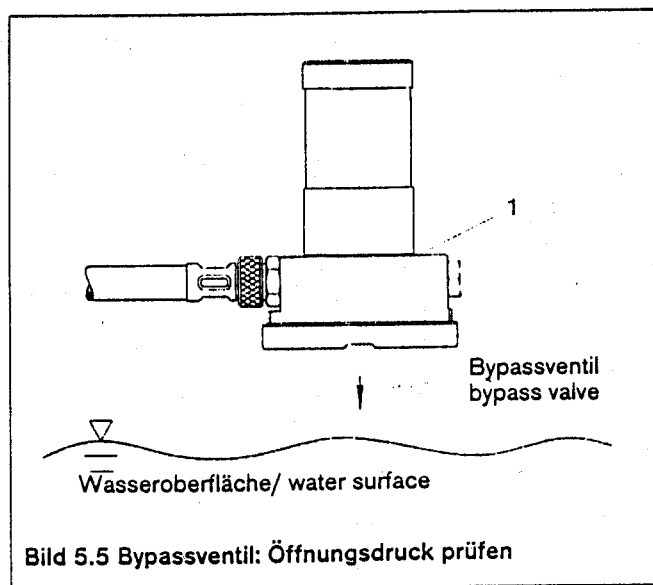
Bypassventil: Öffnungsdruck prüfen
